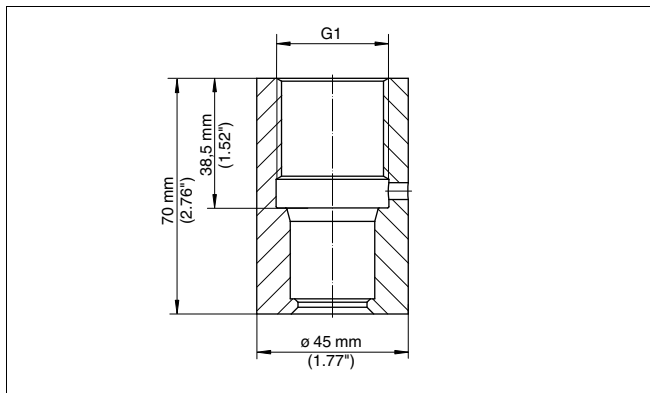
Размеры приварного штуцера G1" для применения для PASVE
